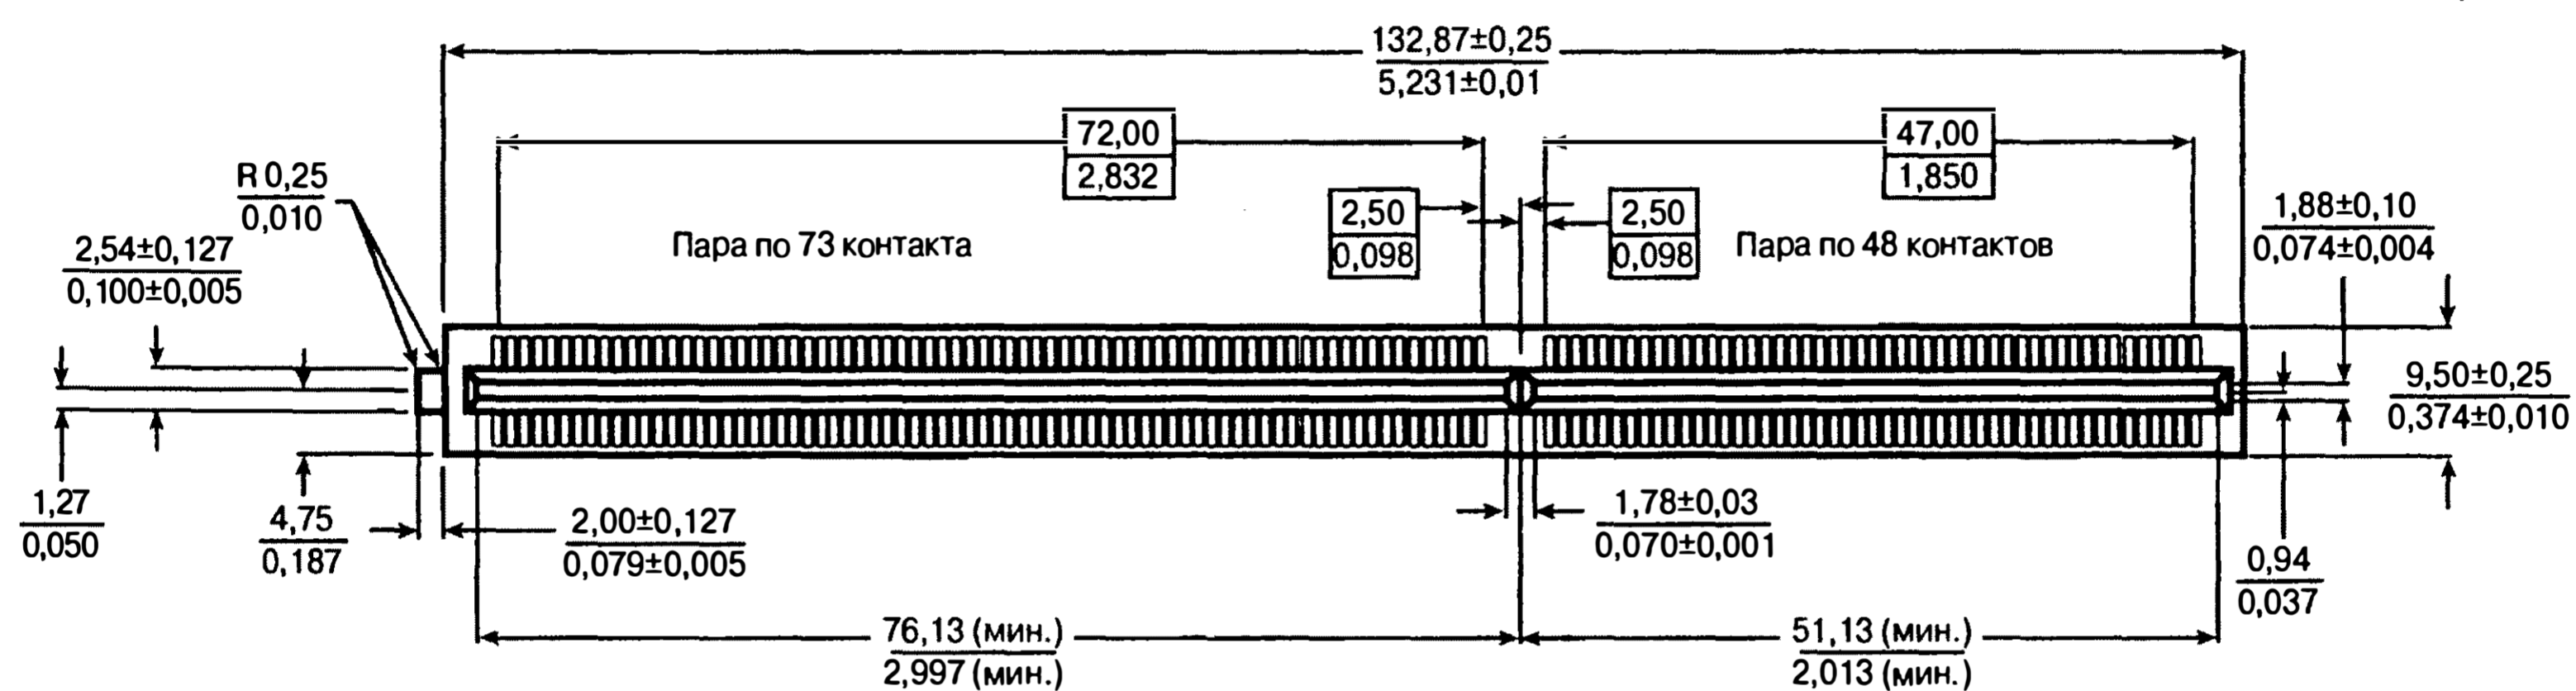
Размеры разъема Slot 1 для процессора Pentium II
